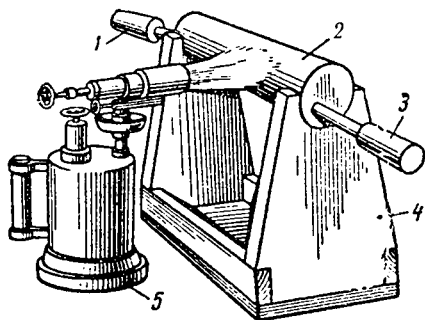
Приспособление для одновременного нагрева нескольких паяльников паяльной лампой
